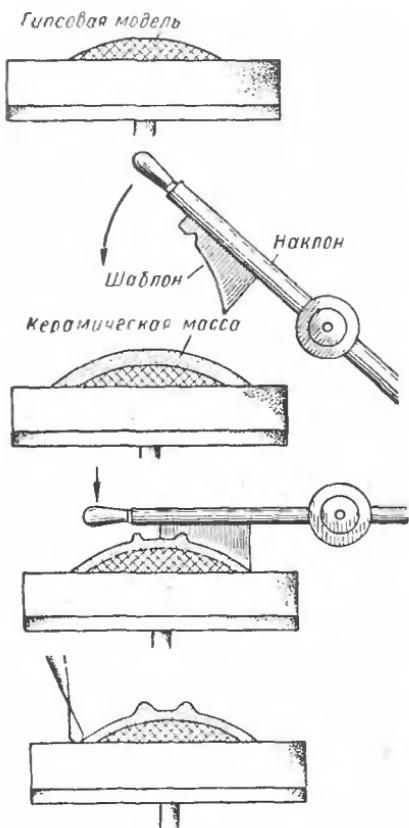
Схема формования плоского изделия на приводном формовочном станке
